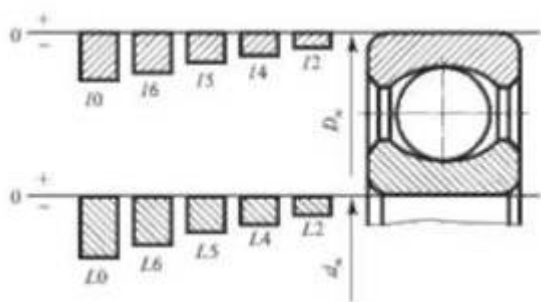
Схема расположения полей допусков на наружный и внутренний диаметр подшипников качения
